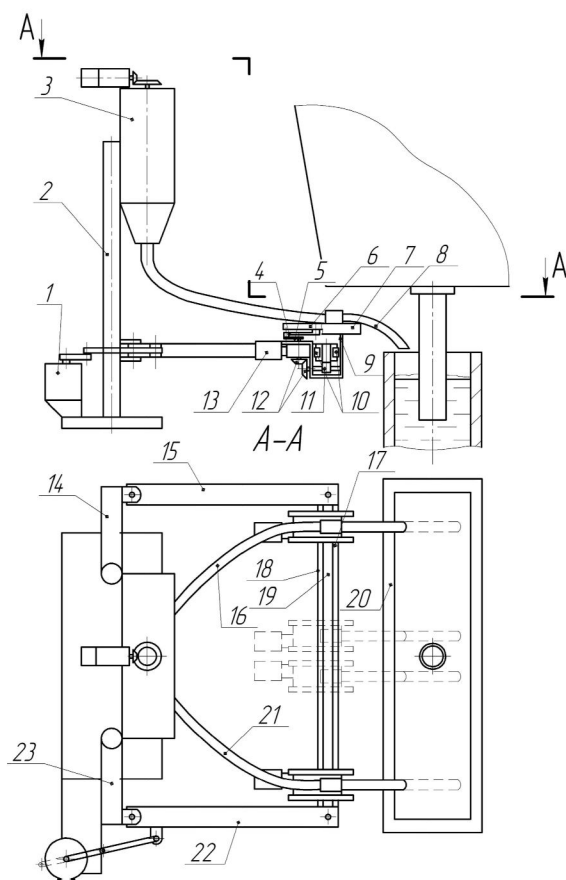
Схема установки, обеспечивающей подачу ШОС в кристаллизатор сверхкрупного сечения
